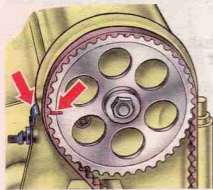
Проверка совпадения установочных меток на шкиве коленчатого вала и крышке масляного насоса
